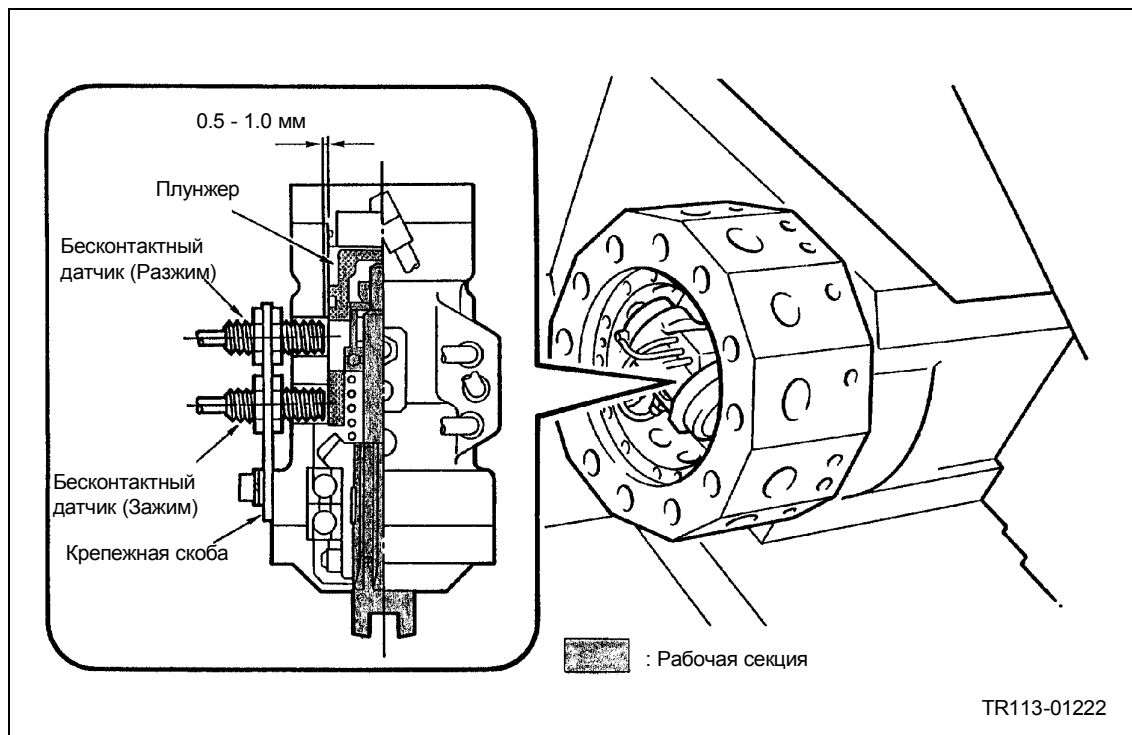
Регулировка бесконтактных датчиков в фрезерном соединении
